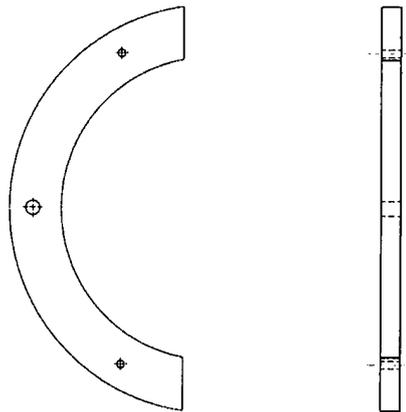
Demi-disques en acier pour supporter les éprouvettes
